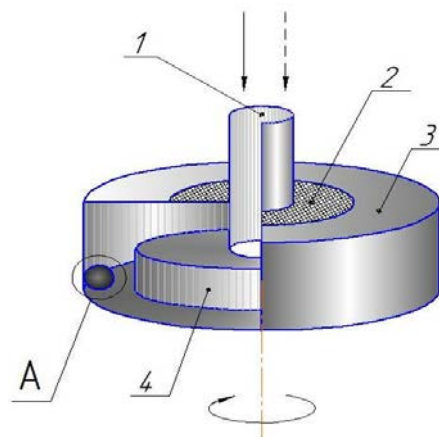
Схема РВМТП: 1 – патрубок ввода материала и несущей среды; 2 – классификатор; 3 – помольная камера; 4 – наружный ротор
